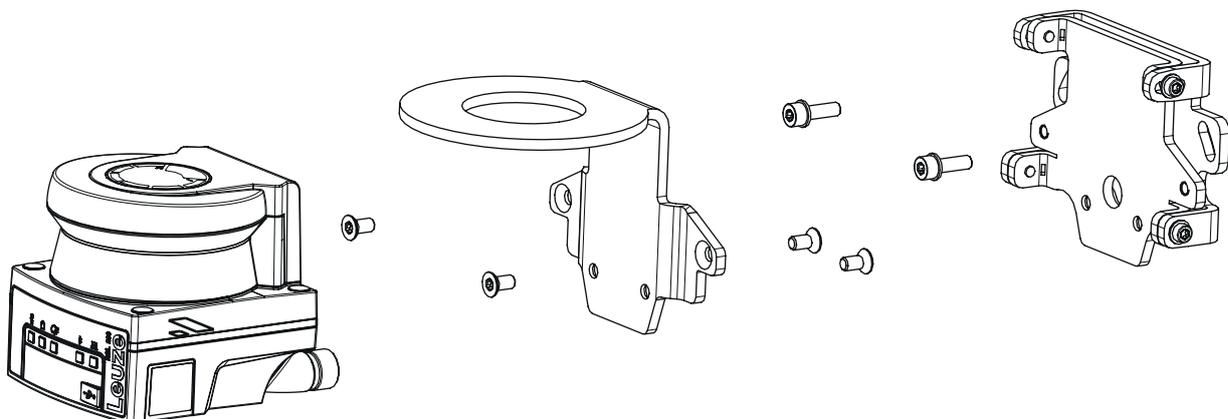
Montagem com suporte de parede e estribo de proteção
